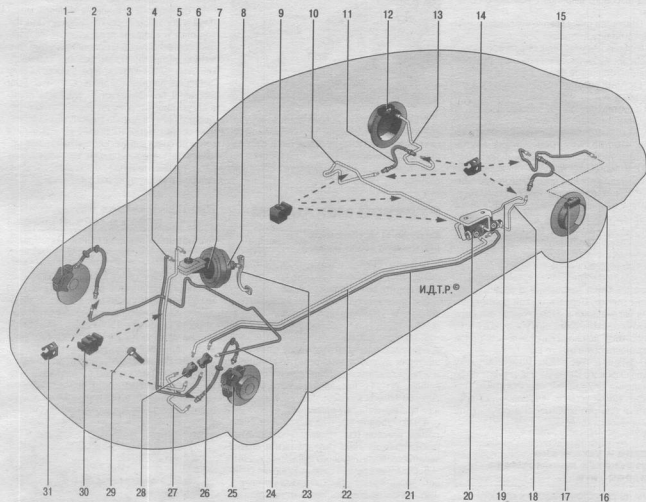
Схема гидропривода тормозов (без антиблокировочной системы): 1 — тормозной механизм правого переднего колеса; 2 — гибкий шланг тормозного механизма правого переднего колеса; 3, 4, 15, 18, 21 — труборазветвитель контура правый передний — левый задний тормоза; 5, 10, 13, 22, 27 — труборазветвитель контура левый передний — правый задний тормоза; 6 — бачок главного цилиндра гидропривода тормозов; 7 — главный цилиндр гидропривода тормозов; 8 — вакуумный усилитель; 9, 30 — держатели труборазветвителей; 11 — гибкий шланг тормозного механизма правого заднего колеса; 12 — тормозной механизм заднего левого колеса; 13, 31 — скобы крепления гибких шлангов; 16 — гибкий шланг тормозного механизма левого заднего колеса; 17 — тормозной механизм заднего левого колеса; 19 — упругий рычаг привода регулятора давления; 20 — регулятор давления; 23 — педаль тормоза; 24 — гибкий шланг тормозного механизма левого переднего колеса; 25 — тормозной механизм левого переднего колеса; 26 — тройник контура правый передний — левый задний тормоза; 28 — тройник контура левый передний — правый задний тормоза; 29 — болты крепления тройников
